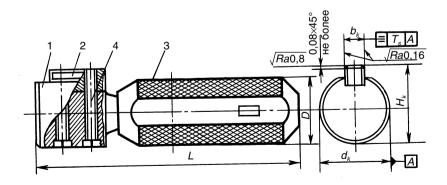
Комплексный калибр для контроля шпоночных пазов
